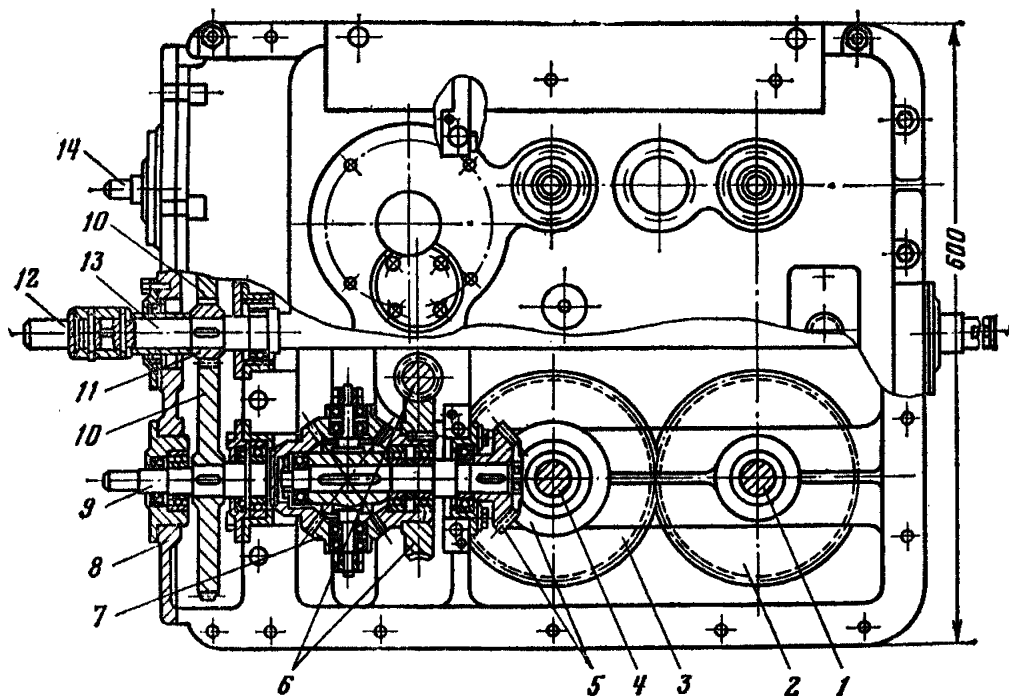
Редуктор привода аппарата АЗК-1:
